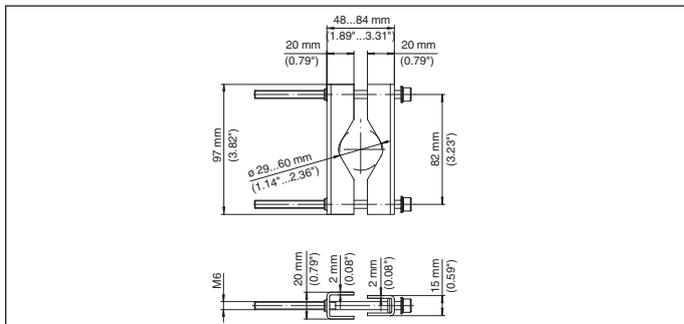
Dimensiones bridas para montaje en tubería VEGAMET 841, 842
